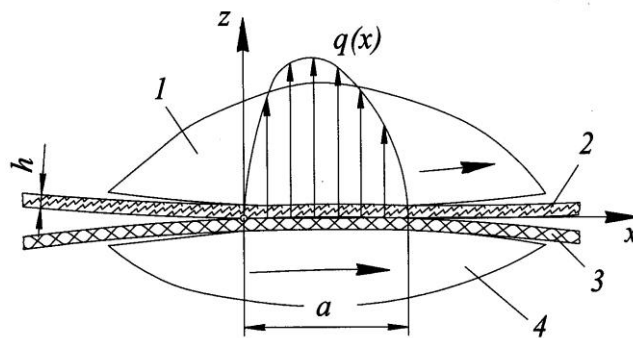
Схема прессового захвата: 1 – верхний вал;
